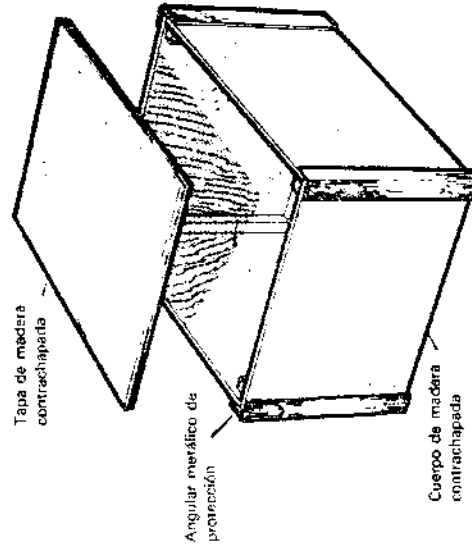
Caja de madera contrachapada, con angulares metálicos de protección
